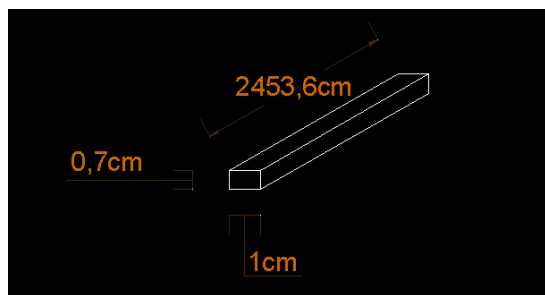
Dimensiones geométricas del conductor de baja tensión.
